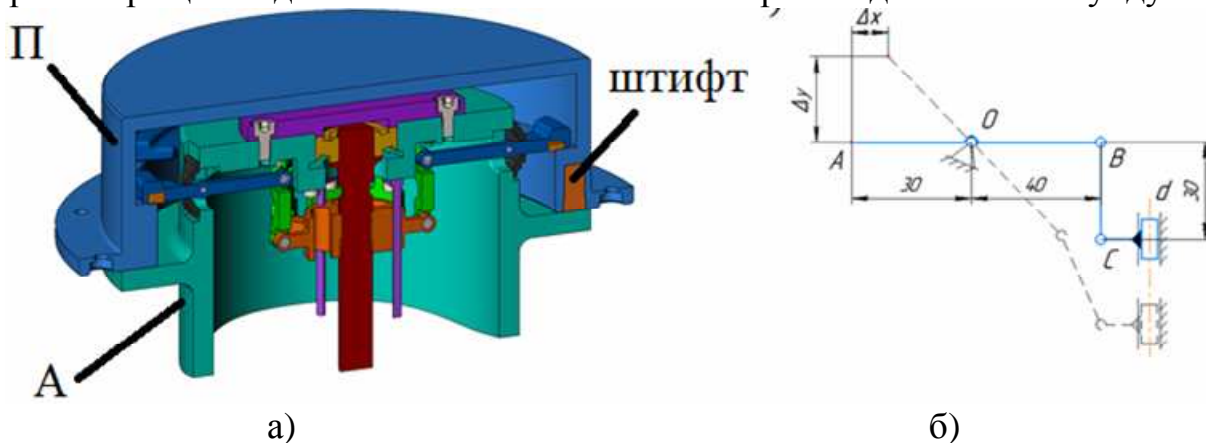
Вид стыковочного агрегата в сцепке и кинематическая схема зажима:
